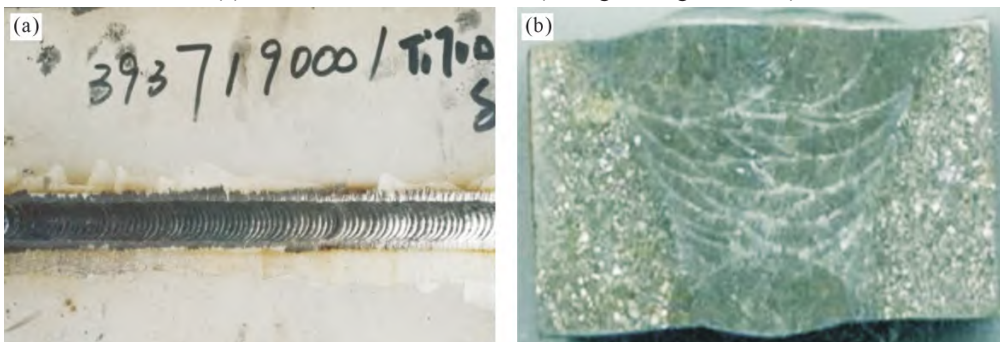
2# 合金试板对接焊缝形貌:(a)TIG 补焊外观;(b)焊缝断面形貌
